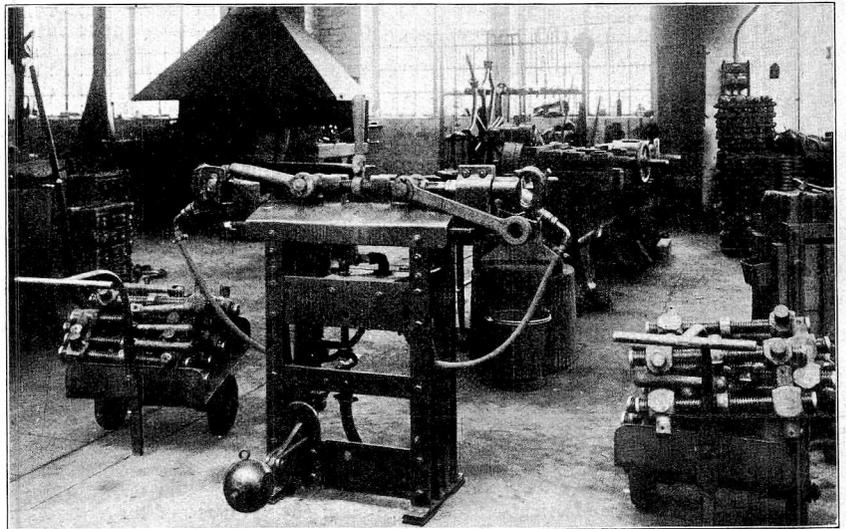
Maschine zum Warmaufrichten des Muttergewindes.
